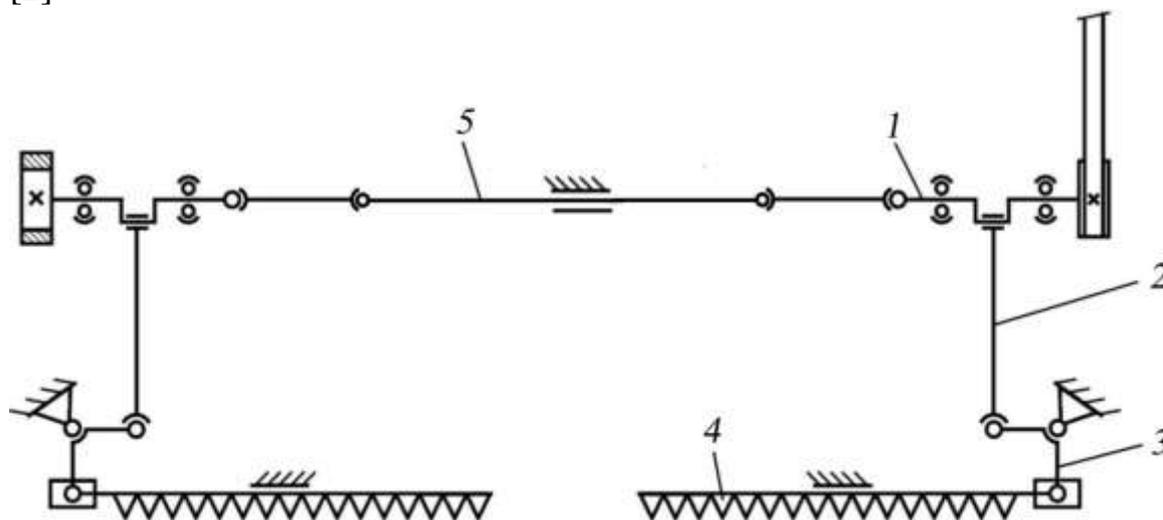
Схема привода двухножевого режущего аппарата с кривошипно-коромысловыми механизмами
